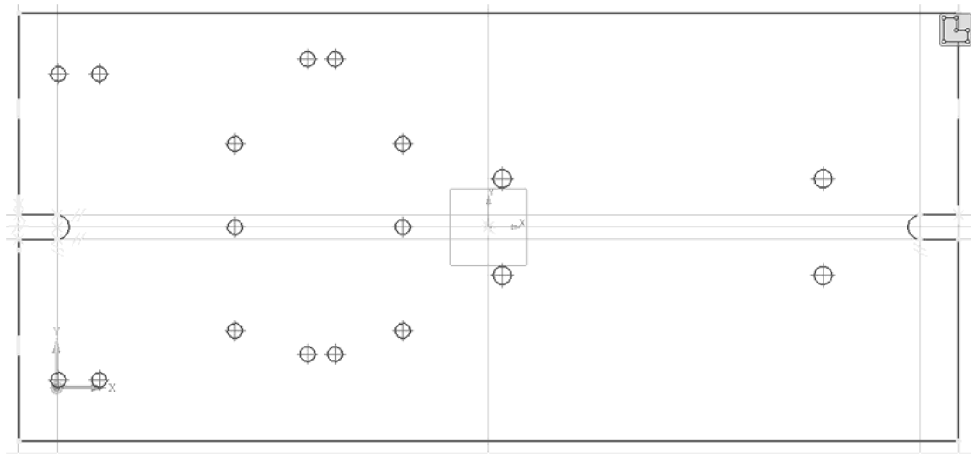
Створення основної частини деталі корпус (операція витиснення)
